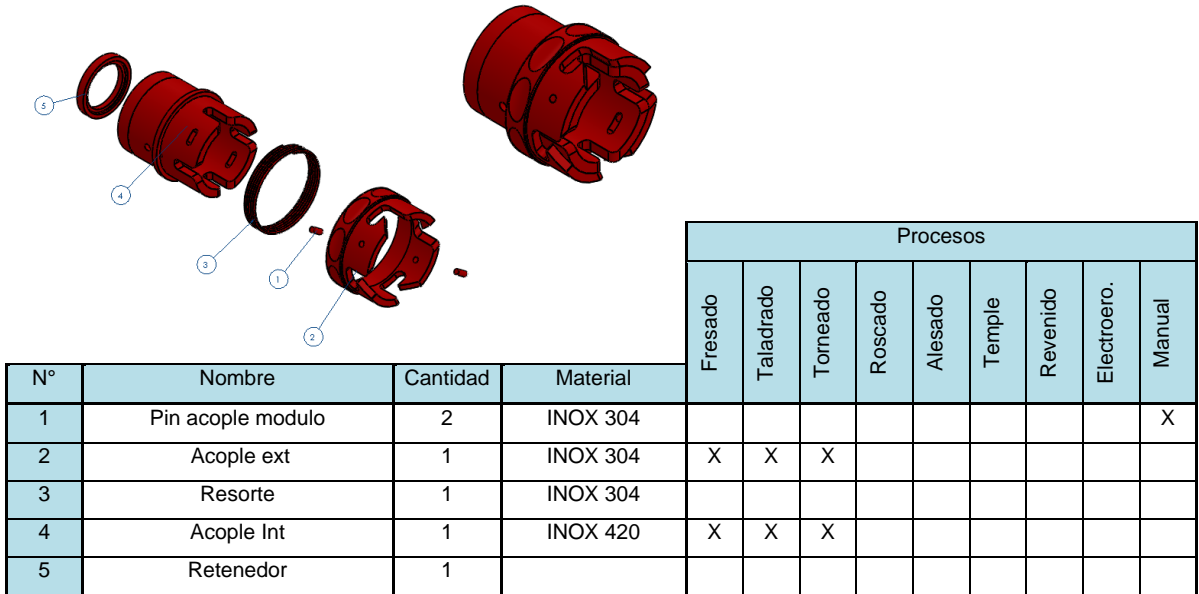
Vista explosionada del subensamble de la reducción trasera
